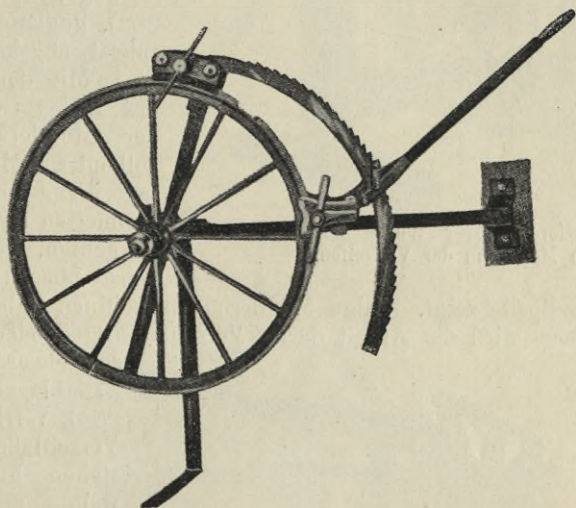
Morgan & Wrights Maschine zum Schließen der Vollreifen.
